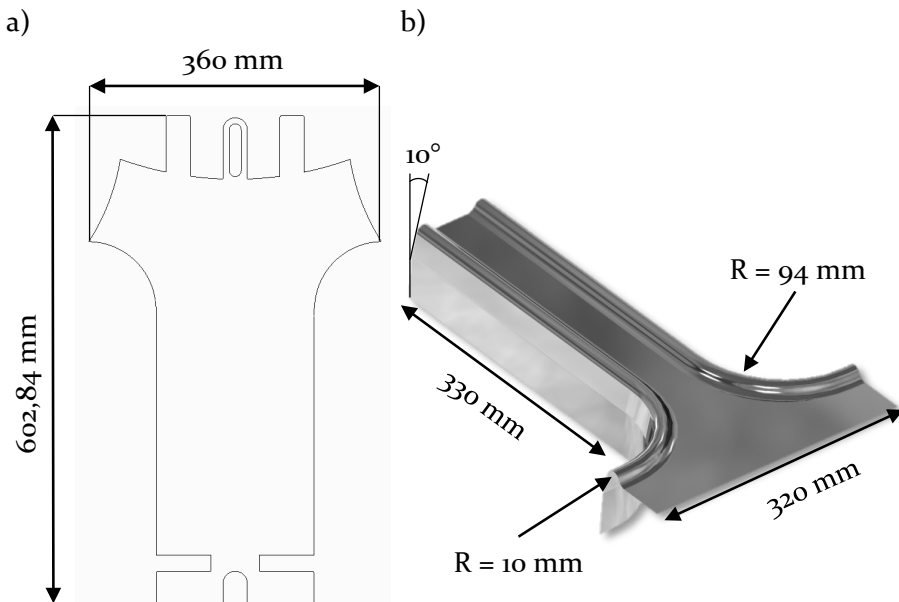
Platinenzuschnitt (a) und Bauteilgeometrie (b) des Demonstratorbauteils
